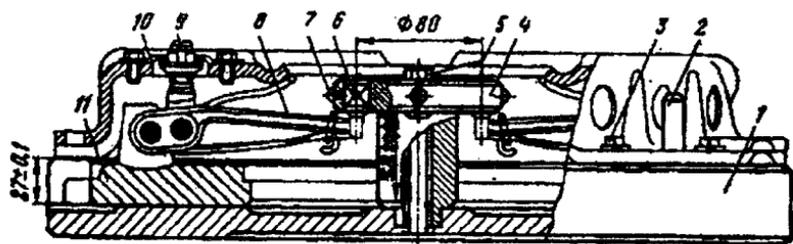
Стенд для разборки, сборки и регулировки сцепления ЯМЗ:
